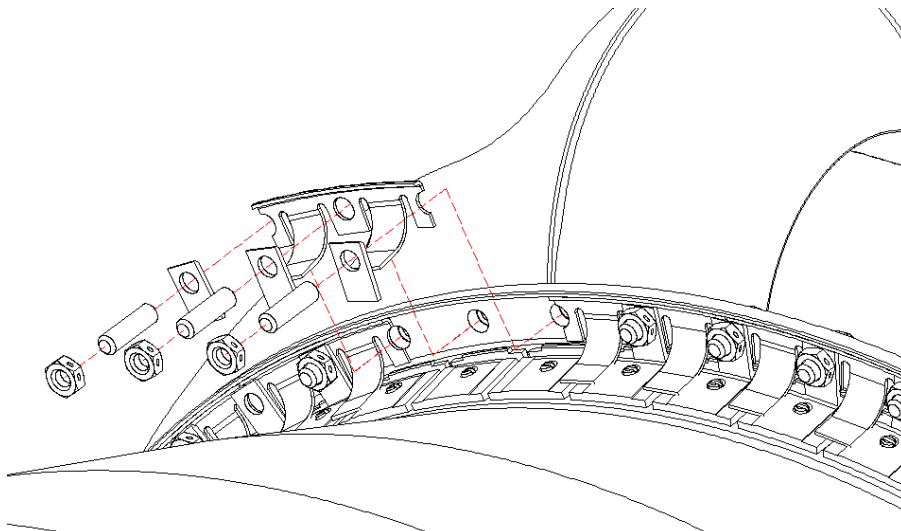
Узел стыка соплового насадка из УУКМ с корпусом камеры
